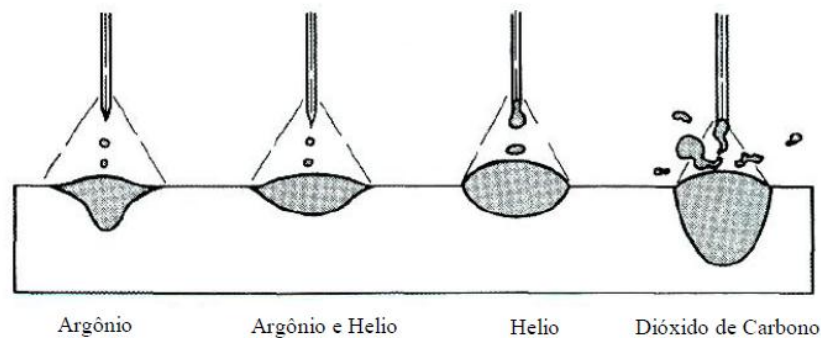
Perfil do cordão e penetração utilizando diferentes tipos de gás em soldagem MIG/MAG [ALVES, 2009].
